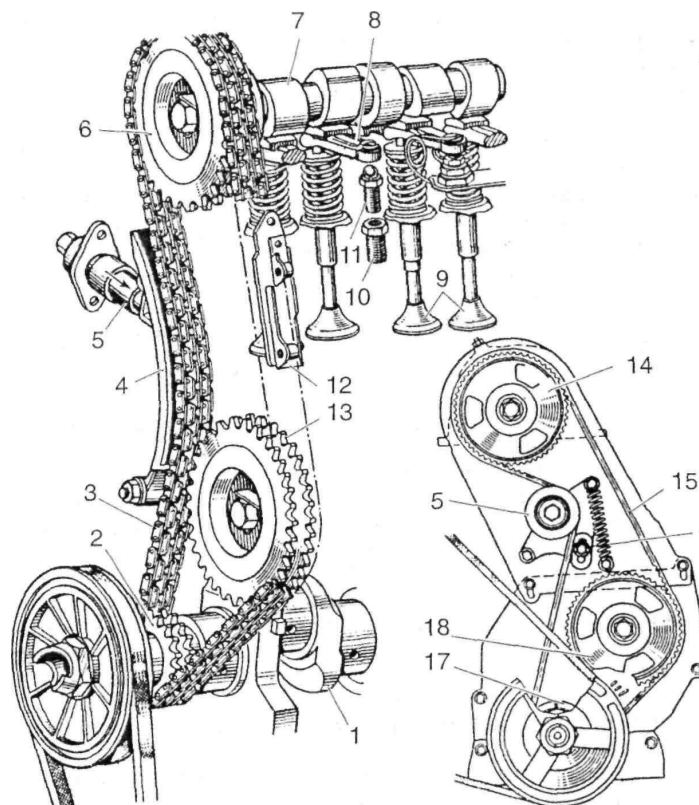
Рис 1.14 Привод механізму газорозподілу двигунів з верхнім розташуванням розподільного вала:
